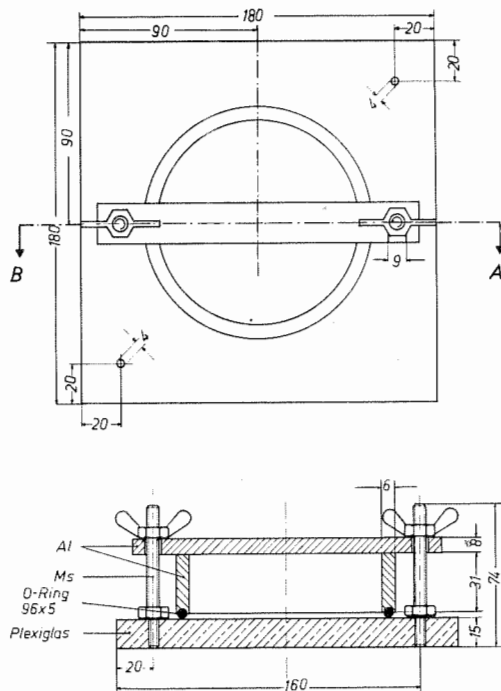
Schemazeichnung der Prüfapparatur. Oben: Grundriß; unten: Schnitt A—B.
